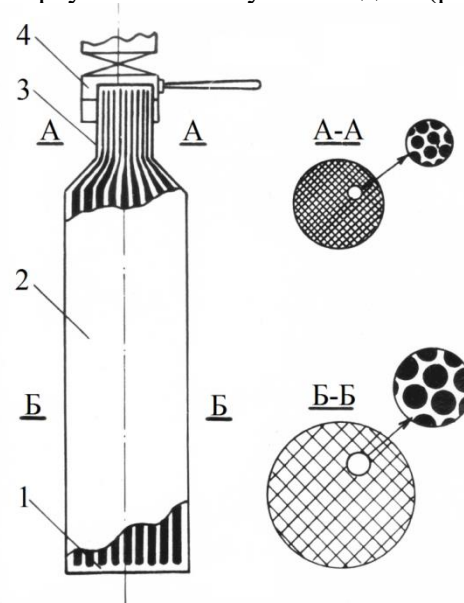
Конструкція пористого балона: 1 – капіляри циліндричної форми; 2 – корпус; 3 – горловина; 4 – колектор
